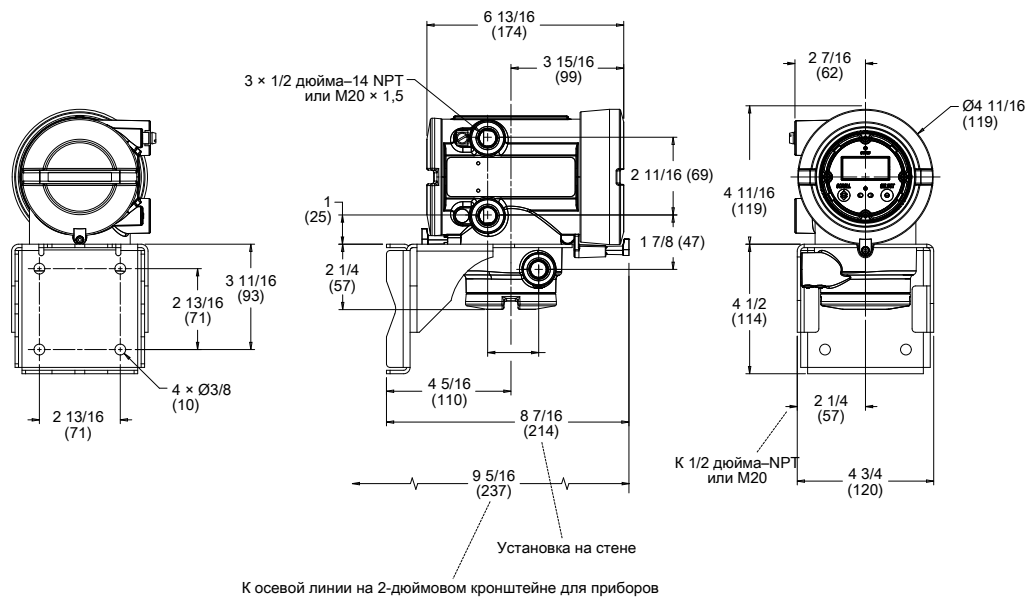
Размеры измерительного преобразователя с 9-проводной удаленной установкой (окрашенный алюминиевый корпус)
